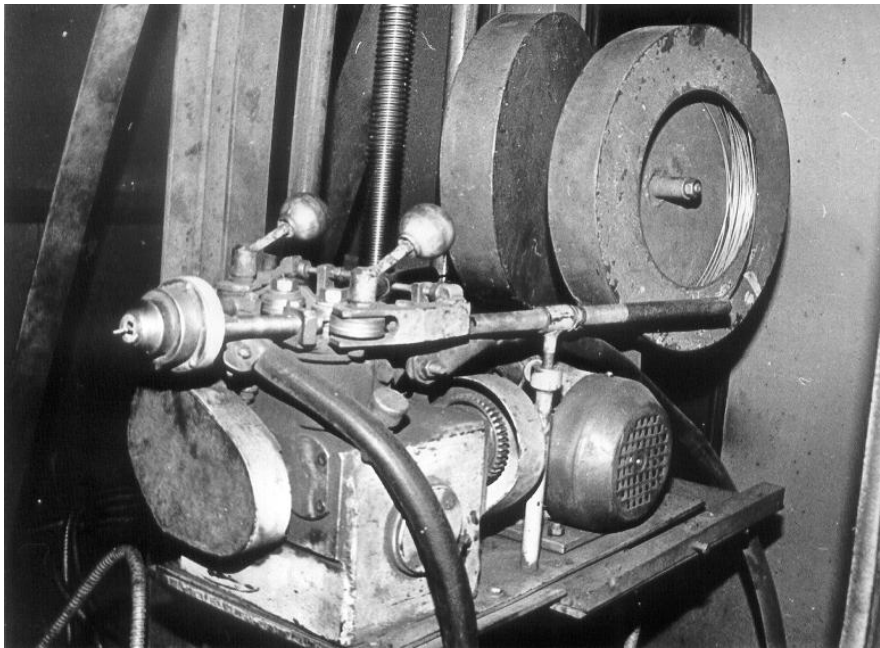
Апарат дугового напilenня: 1 - розпилююча головка, 2 - плита, 3 - корпус, 4 - система подачі дроту, 5 - штативи для касет з дротом, 6 - привід
